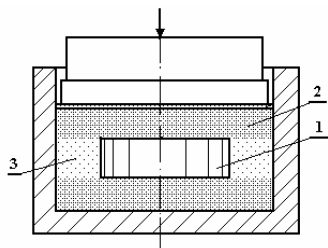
Схема СВС-прессования в неоднородной оболочке: 1 – заготовка; 2 – песчаная оболочка; 3 – кольцевая шамотная оболочка
